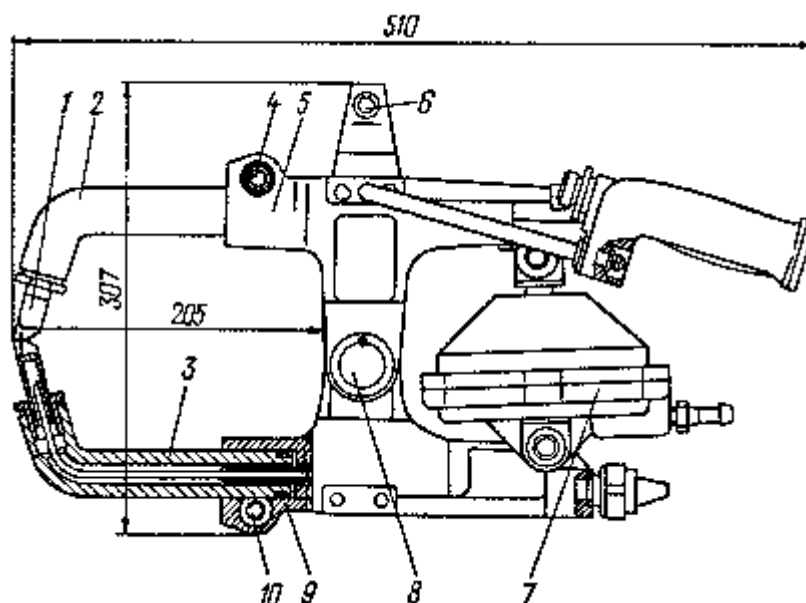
Сварочные клещи типа КТП-8-1
